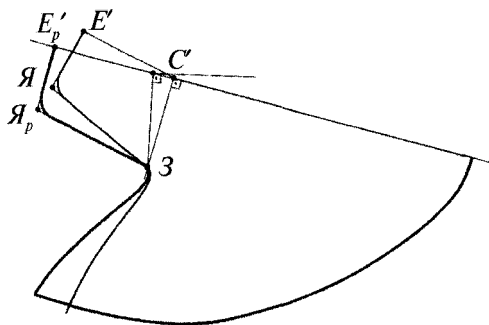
Схема построения конструктивной основы верха полуботинок с боковыми резинками
